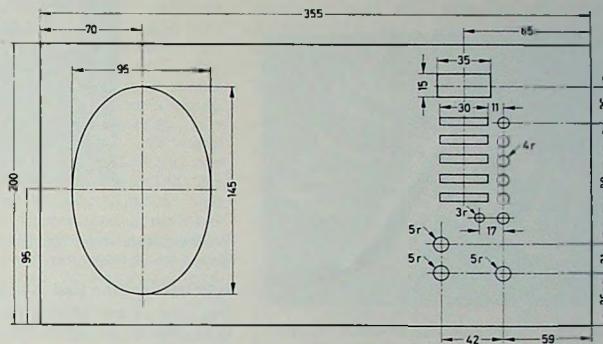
(oben). Abmessungen, Bohrungen und Ausschnitte der Metallfrontplatte des Empfängers
